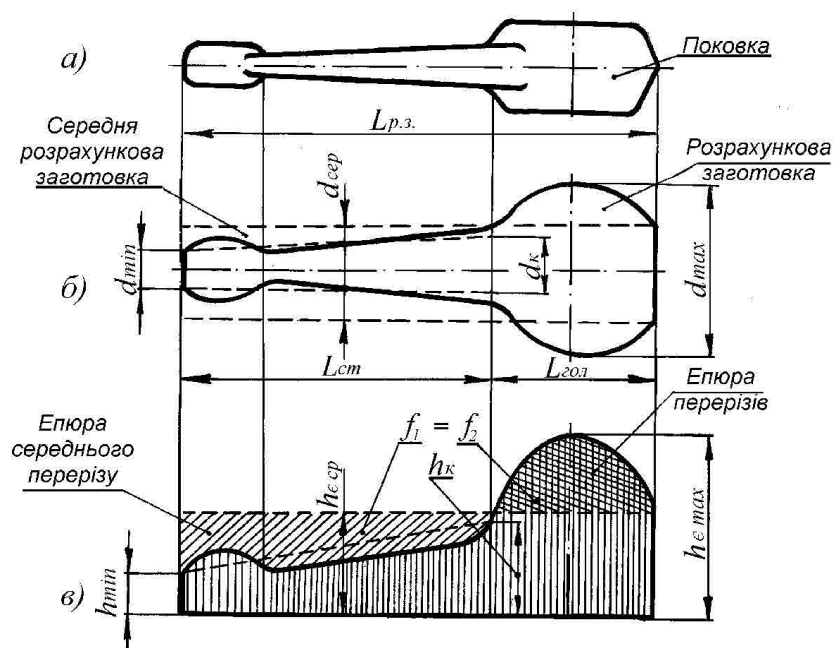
Побудова розрахункової заготовки і епюри перерізів
